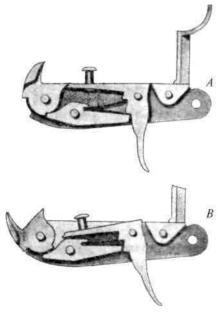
Замок со смонтированными рабочими и вспомогательными деталями Одна из боковых сторон кожуха снята, чтобы показать внутреннее устройство замка
